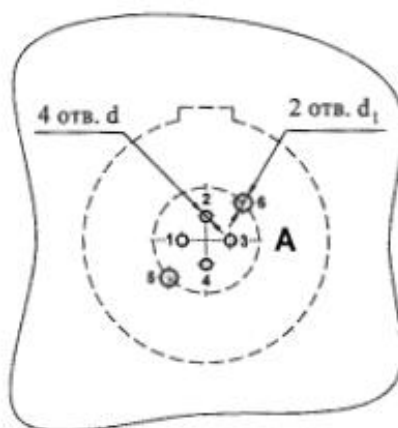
Схема расположения отверстий для установки соединителя СКЦ102-1/9 и СКЦ102-1/11... печатного монтажа
